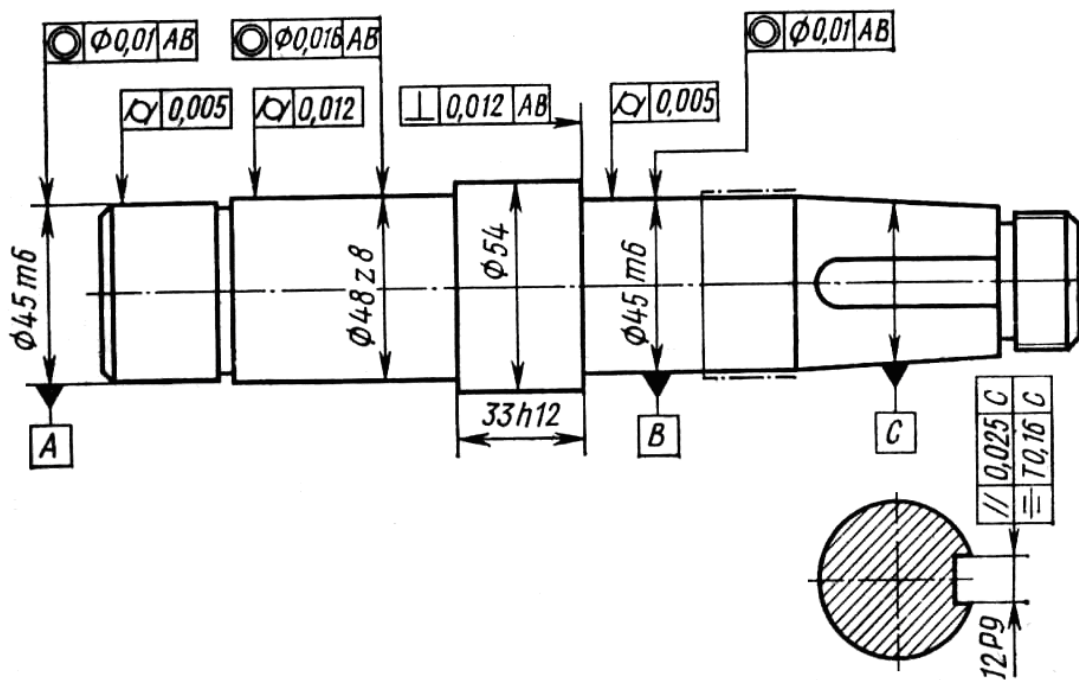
Допуски форми і розташування поверхонь вала
